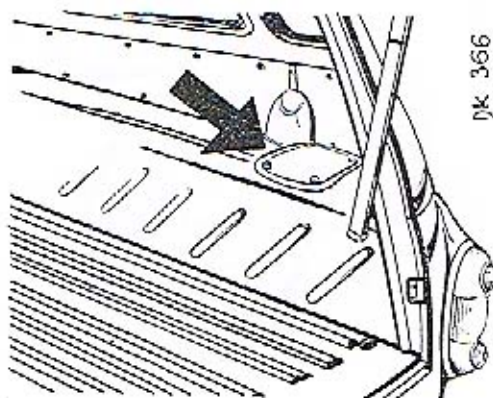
Deckel zum Ausbau des Behälters und des Schwimmers des Kraftstoffmessers.
